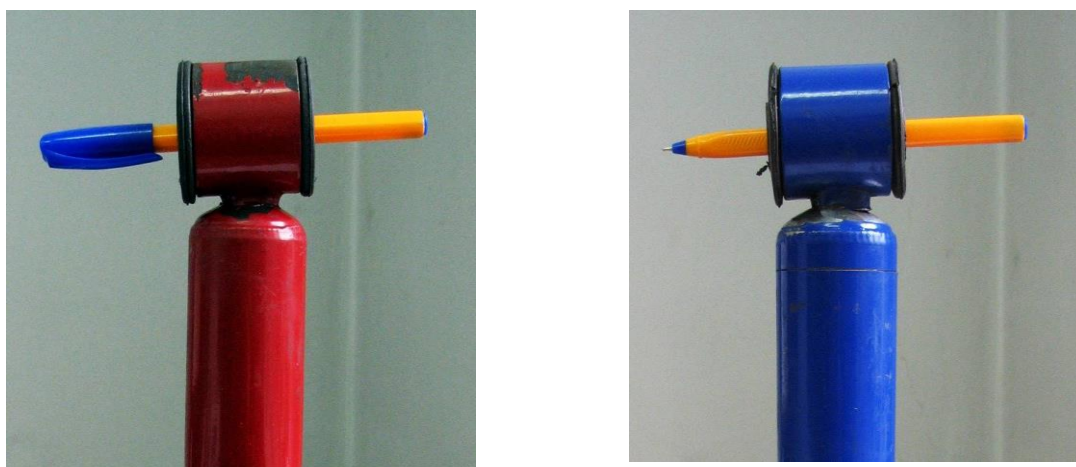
Внешний вид резервуаров амортизатора в сборе после реконструкции
